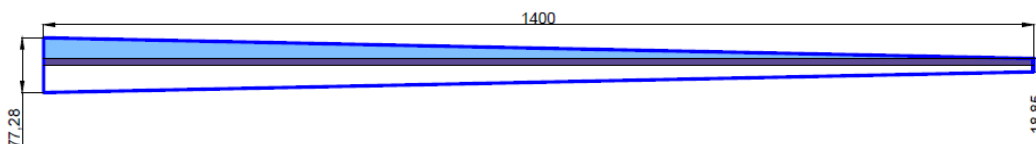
Plancha de chapa dividida, por su mitad, en áreas
